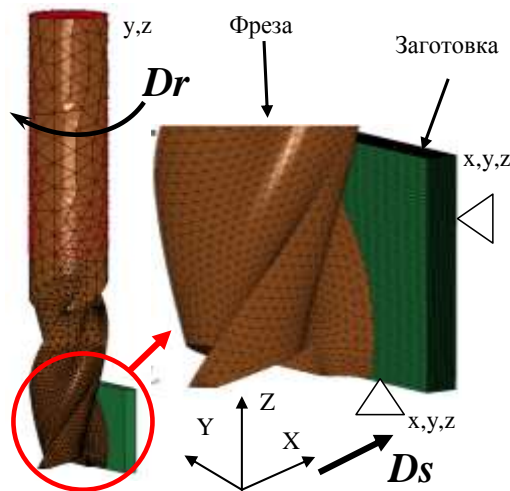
Розрахункова схема 3D-моделі скінченого фрезерування
